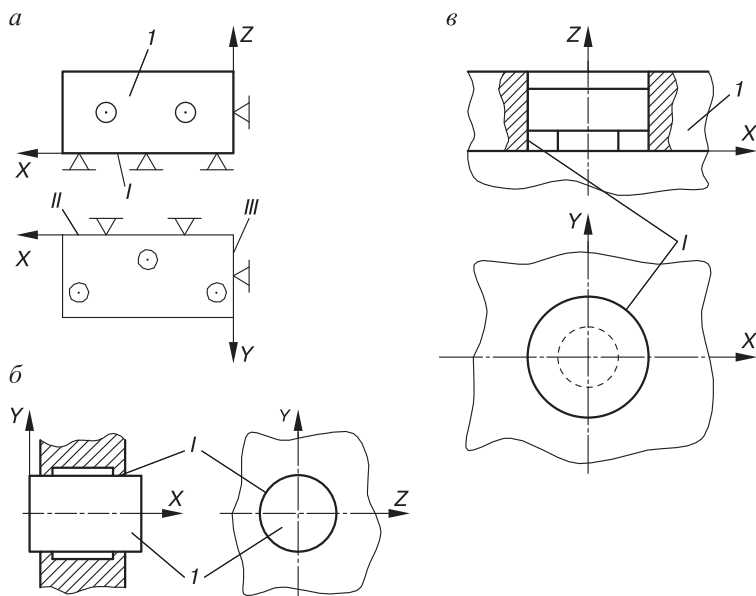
Пример закрепления и обозначения схемы базирования:
